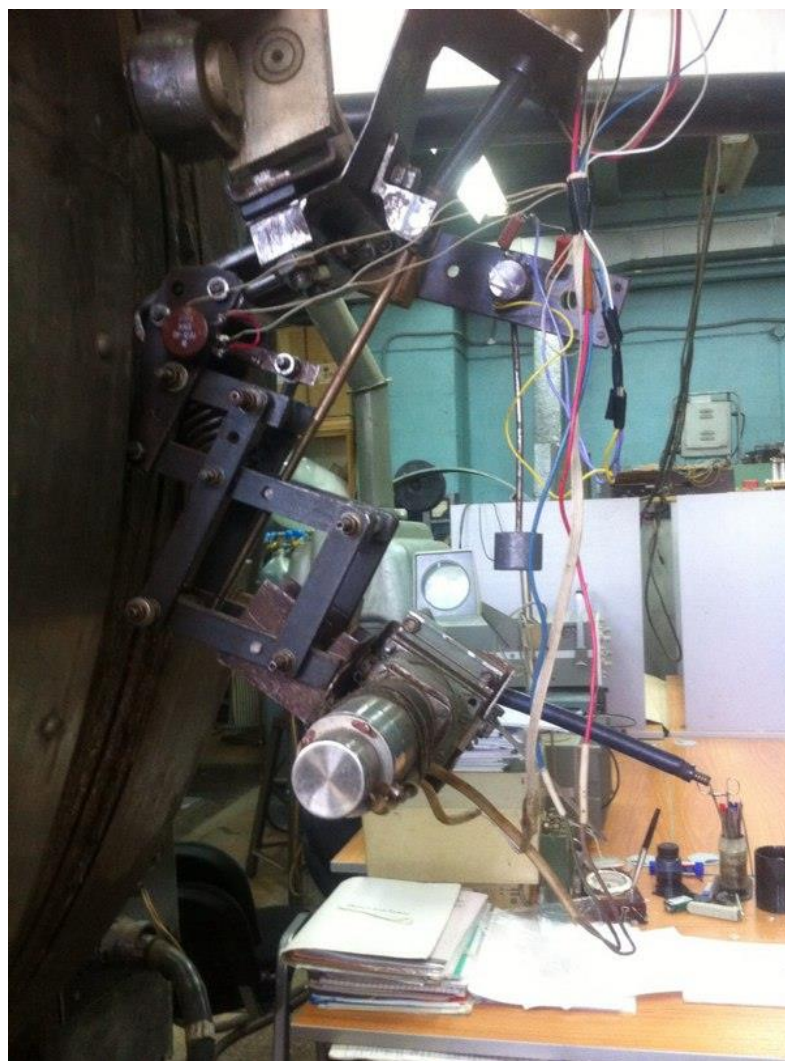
макет (механизм корректировки угла наклона сварочной головки).
